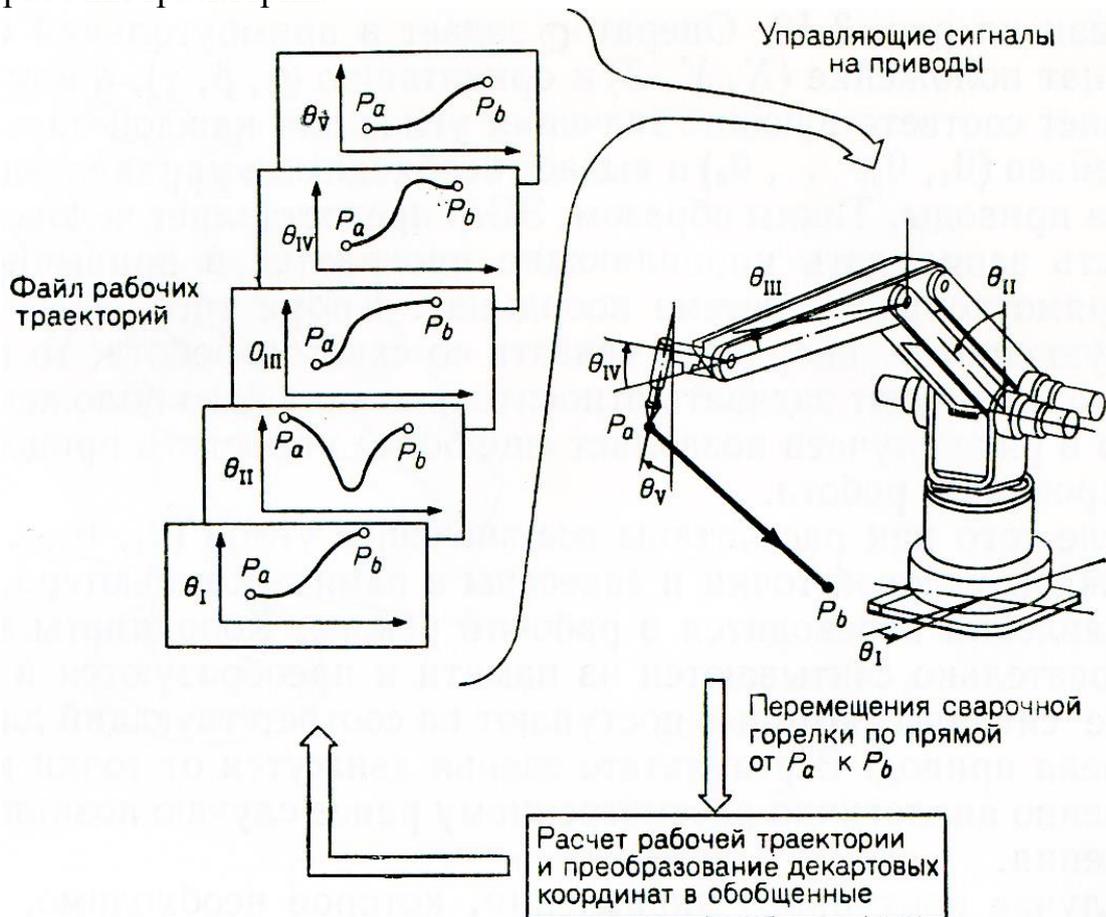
Управление от ЭВМ роботом для дуговой сварки
